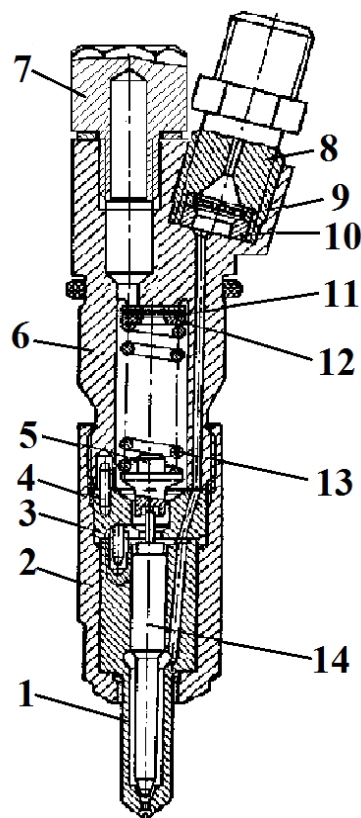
Форсунка дизеля КамАЗ-740 с замкнутым надыгольным объемом: 1 – корпус распылителя; 2 – гайка распылителя; 3 – проставка; 4 – установочный штифт; 5 – штанга; 6 – корпус форсунки; 7 – колпак с дополнительным объемом; 8 – штуцер; 9 – фильтр; 10 – прокладка; 11 и 12 – регулировочные шайбы; 13 – пружина; 14 – игла распылителя
